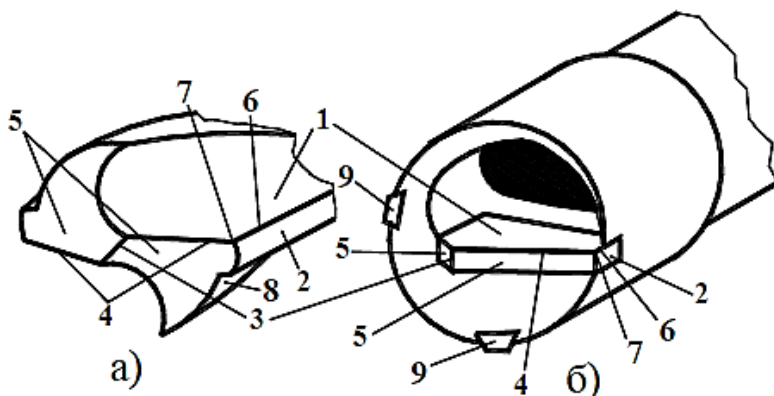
Поверхні робочої частини спірального (а) і одно кромкового (б) свердла. 1 - передня поверхня (Аγ); 2 - допоміжна задня поверхня (А'а) або стрічка; 3 - поперечна ріжуча кромка (КП); 4 - головні (К) ріжучі кромки; 5 - задня поверхня (Аα); 6 - допоміжні ріжучі кромки (К'); 7 - вершина зуба; 8 - спинка зуба; 9 - направляючі елементи.
